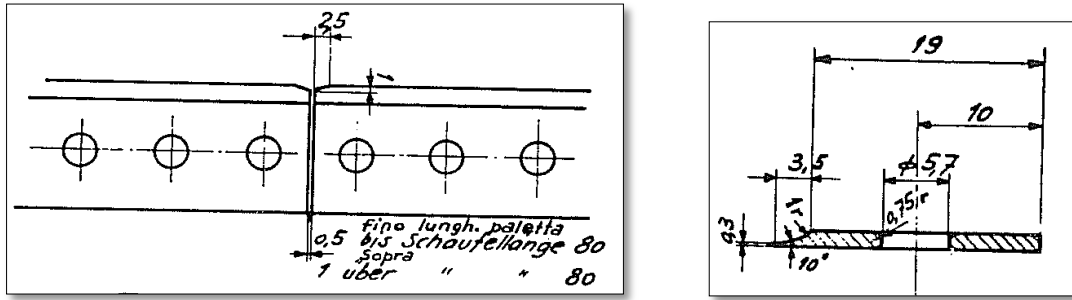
dimensioni del bendaggio del 1° stadio della macchina n° 2.
